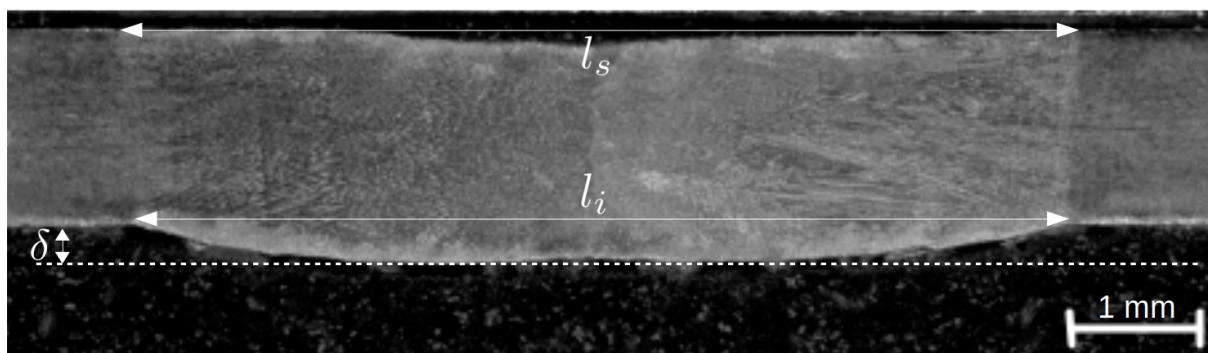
Vue de coupe d'un bain de 316L pour une vitesse de soudage de 2.3 mm/s.
